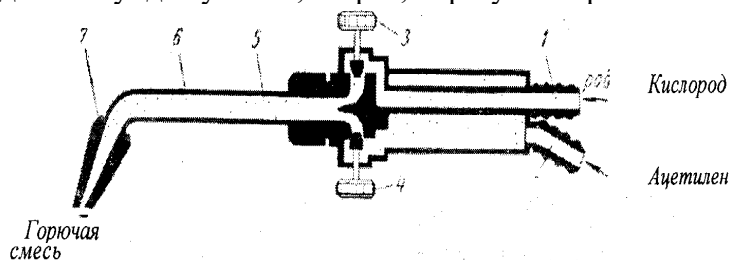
Схема безынжекторной сварочной горелки
